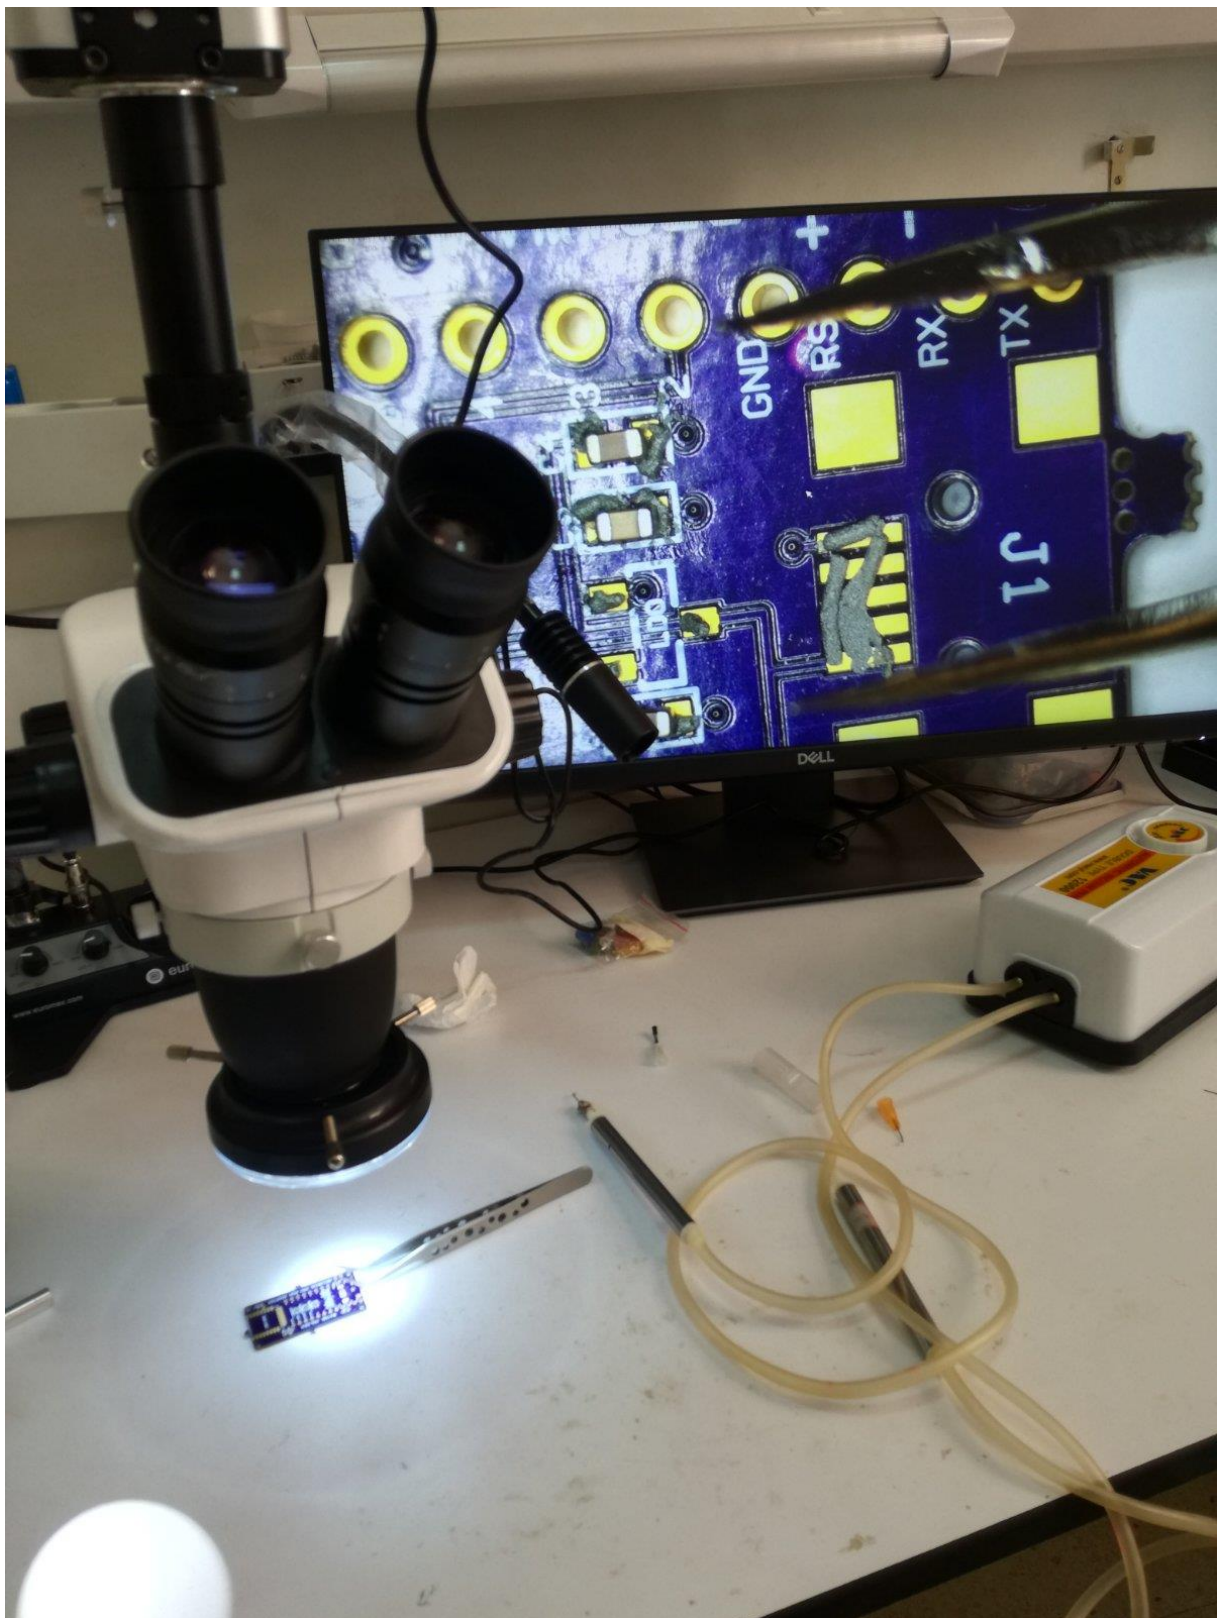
vue du PCB depuis le stéréo-microscope
